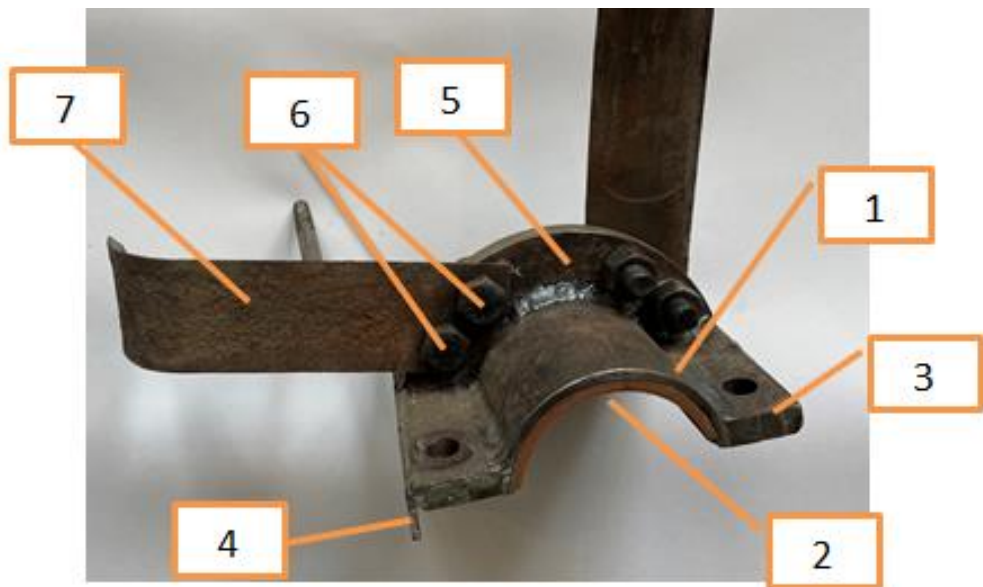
Устройство половинки секции с ножами: 1-корпус; 2- фрикционная накладка; 3 – полка корпуса; 4- щиток; 5- фланец; 6 – болты; 7- нож.
